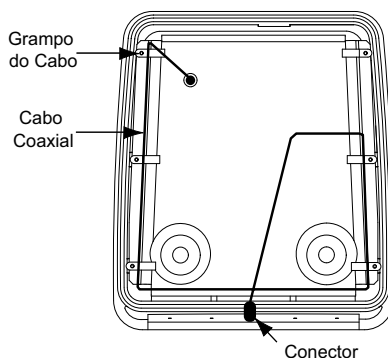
Roteamento do Cabo Coaxial do GPS
